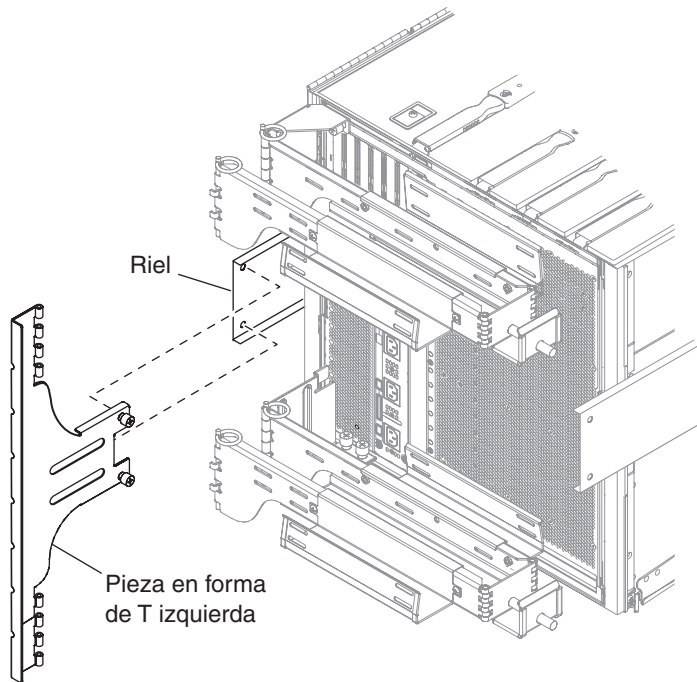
Montaje de la pieza en forma de T izquierda
